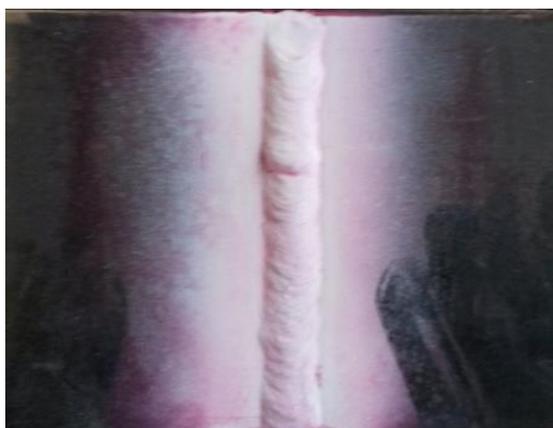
Probeta soldada con electrodo E6011 sacado de su envase
